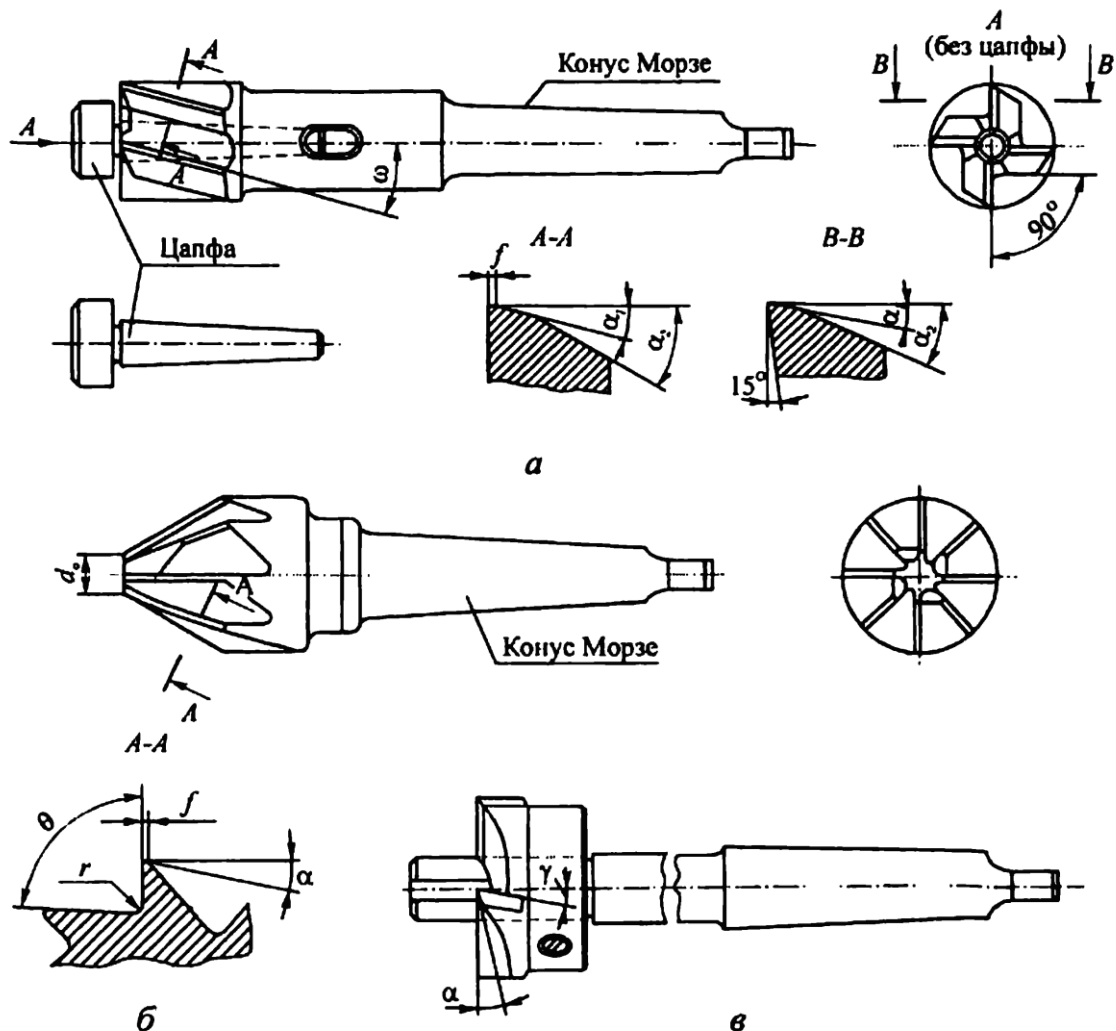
Зенковки: *а* – для цилиндрических углублений; *б* – для подрезания торцов
